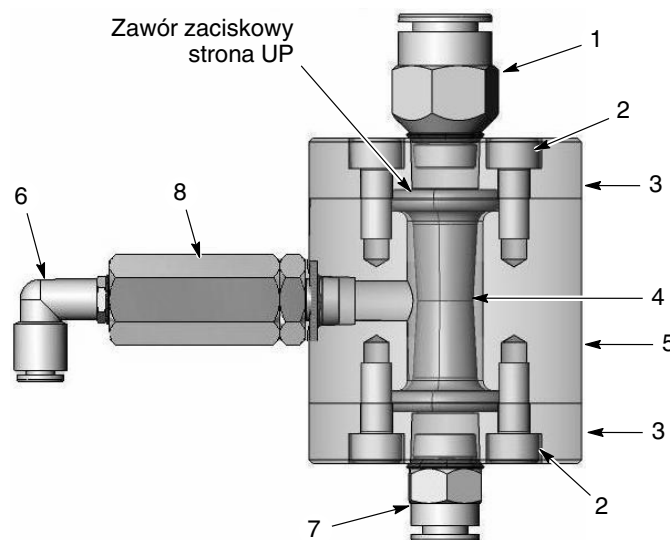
Widok rozstrzelony rozdzielacza
